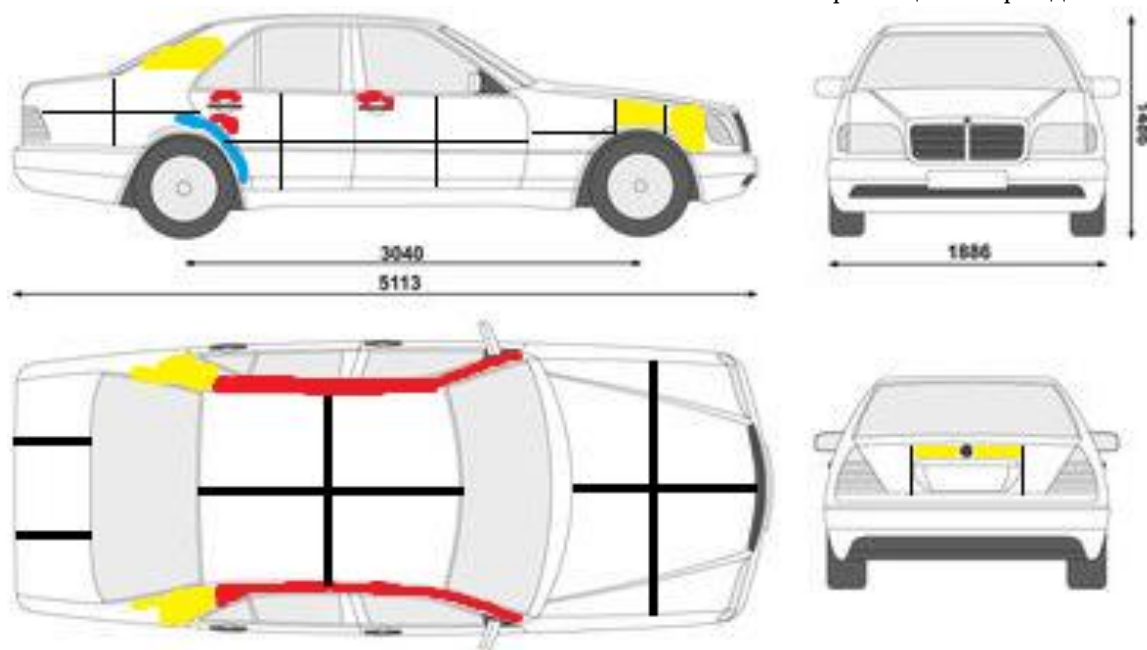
Вид автомобиля с габаритными размерами и условными обозначениями расположения датчиков системы фиксации повреждений
